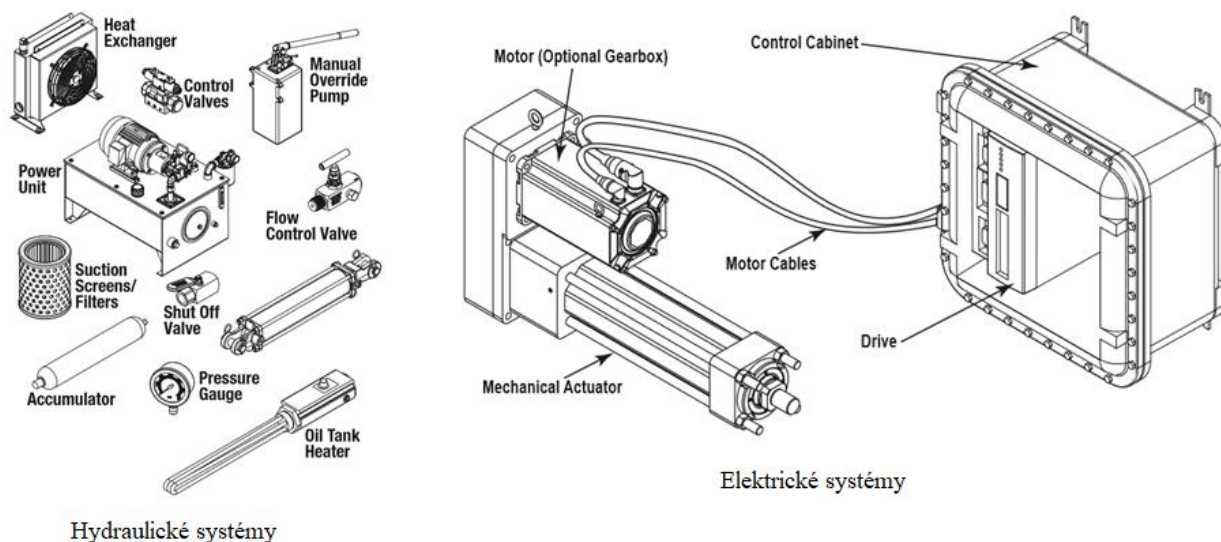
Schéma zapojení hydraulického systému
